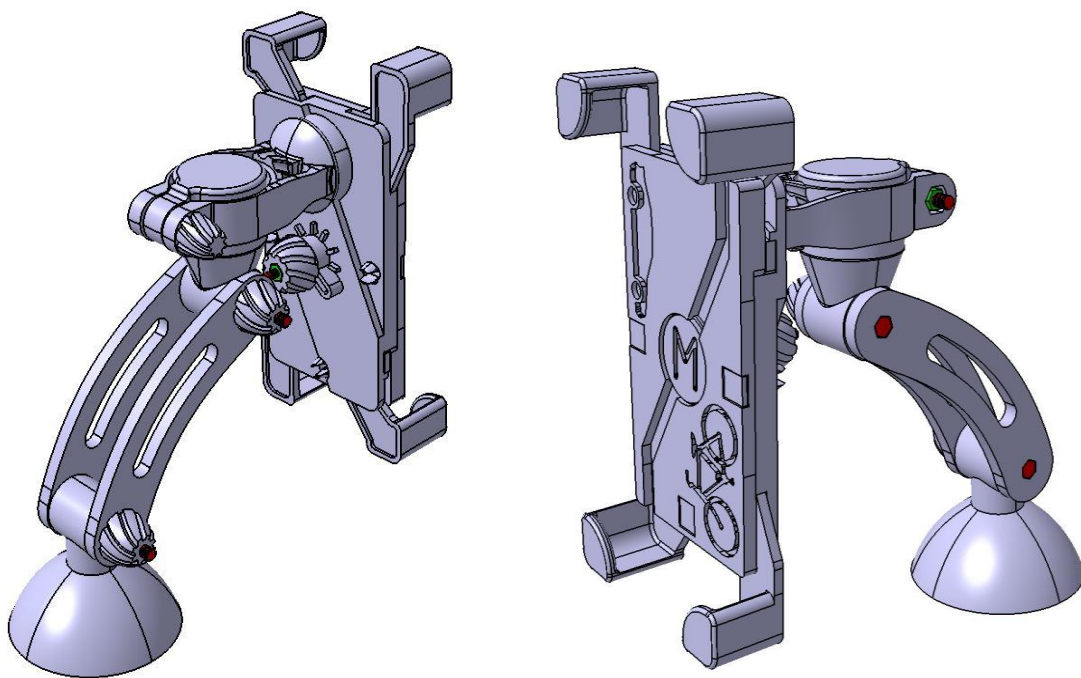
Ensamblaje del diseño final. Rojo: Tornillo Verde: Tuerca
